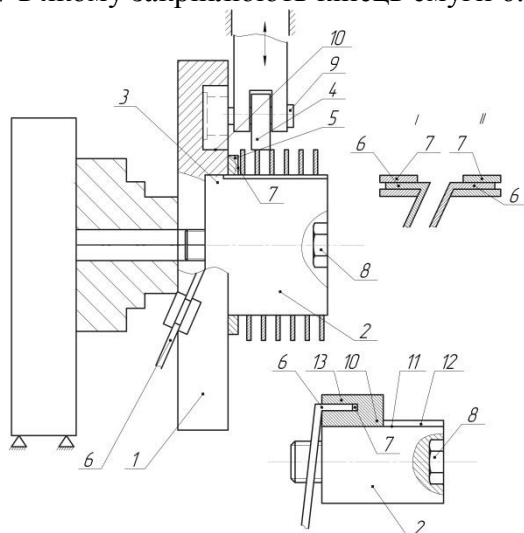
Універсальний пристрій для виготовлення гвинтових заготовок
